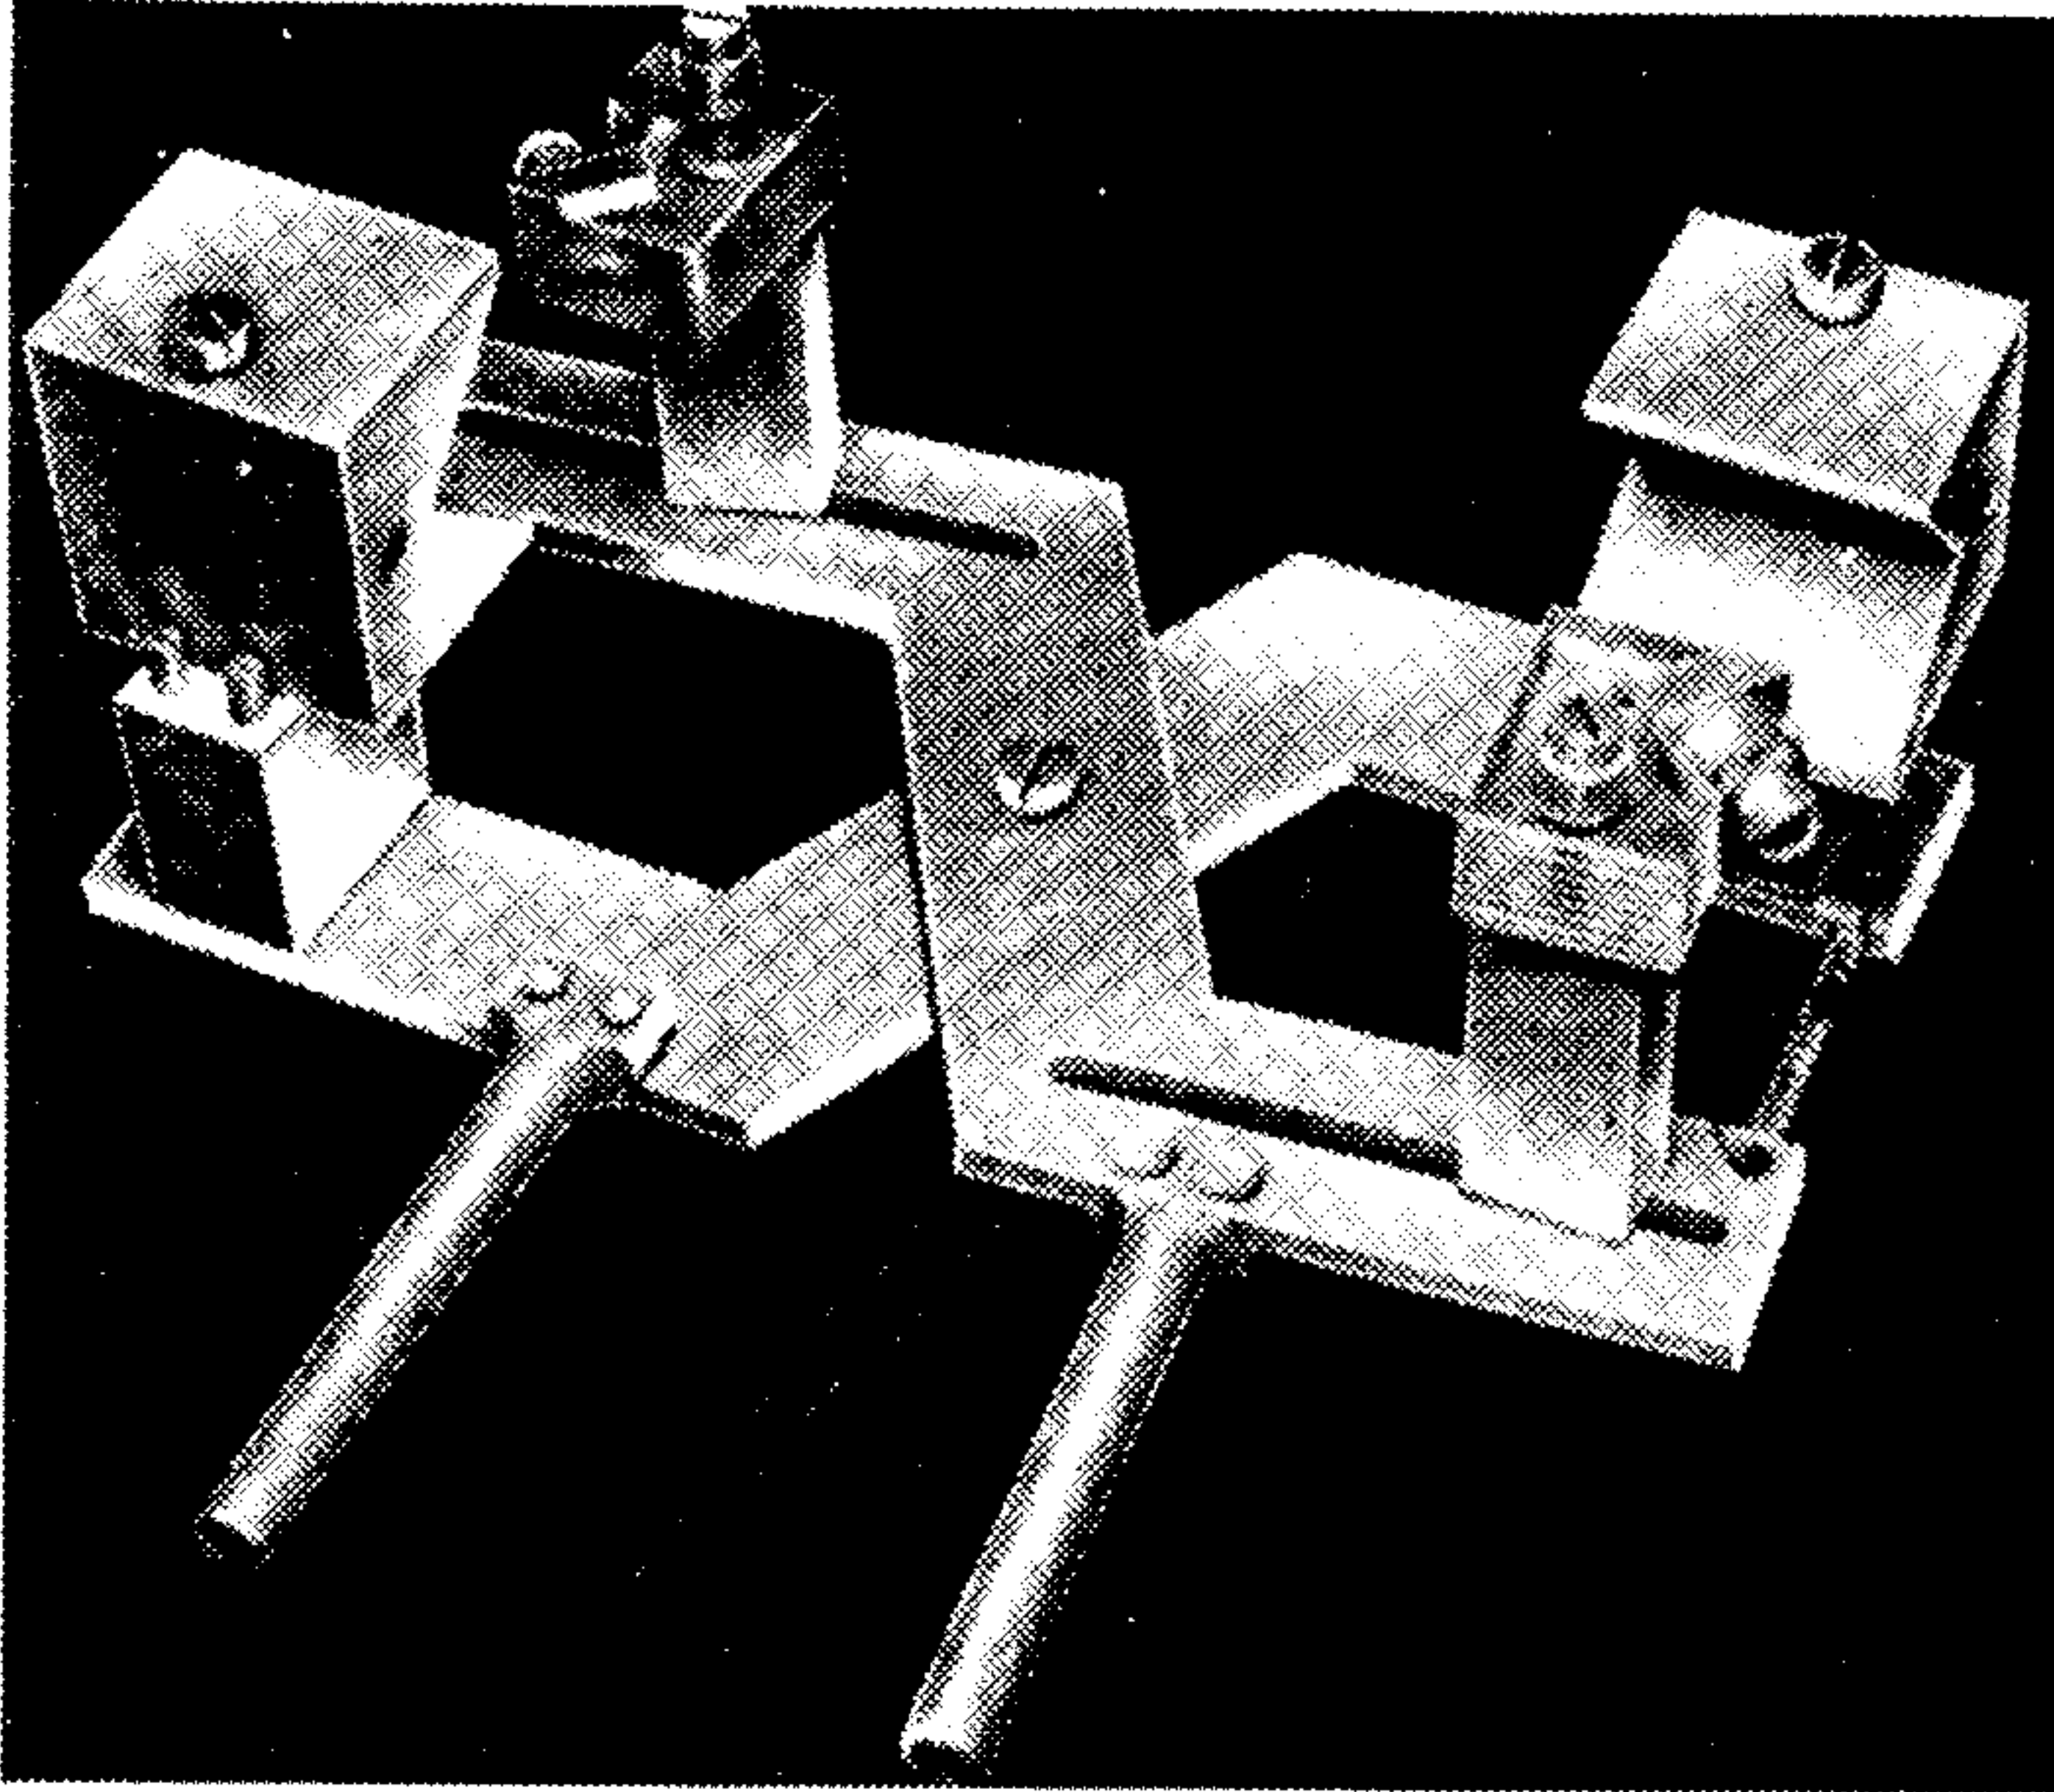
Рис. I Механическое устройство для установки искателей на контролируемое сварное соединение
